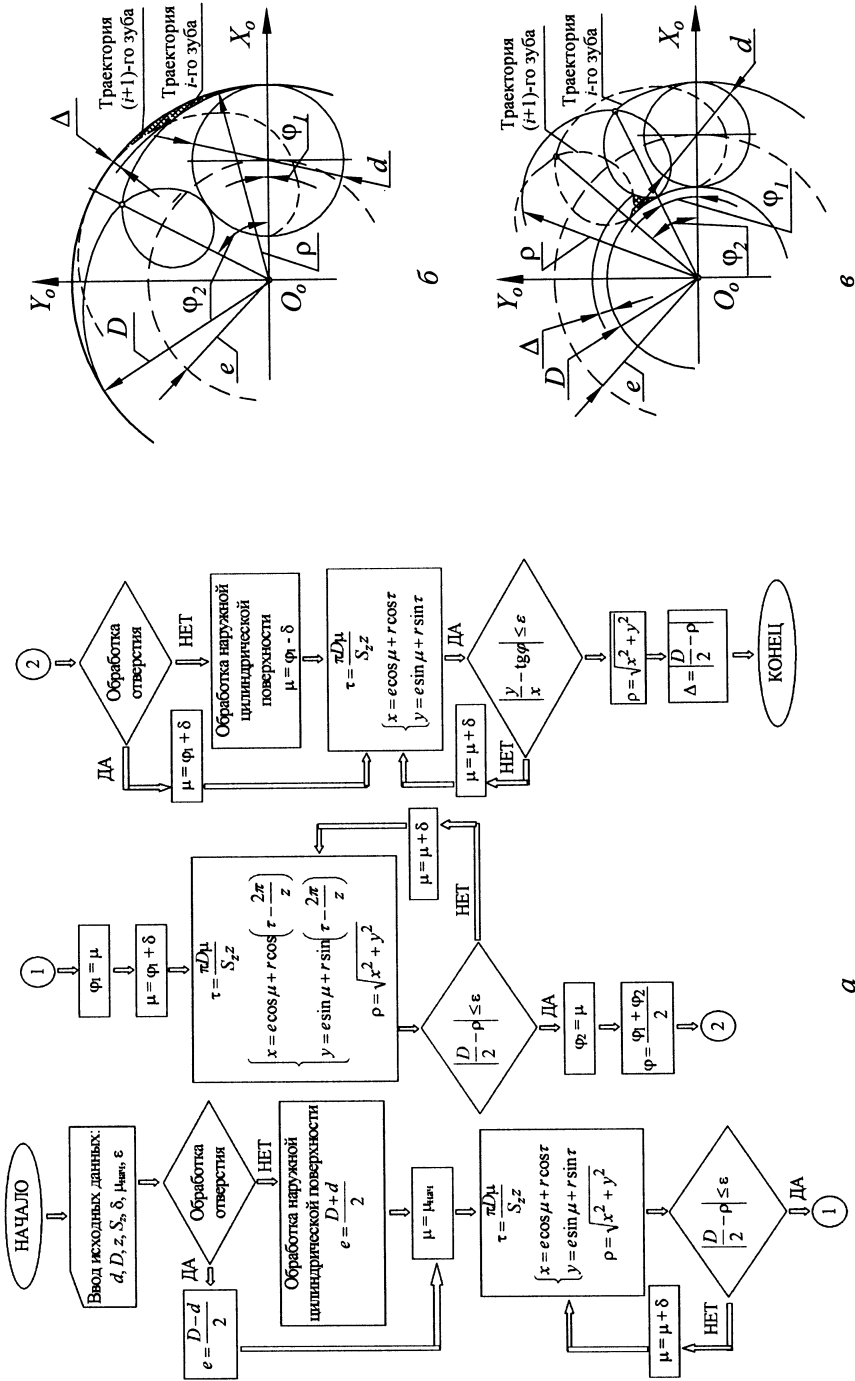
Алгоритм расчета величины огранки при планетарном фрезеровании цилиндрических поверхностей (а) и схемы фрезерования внутренней (б) и наружной (в) поверхностей
